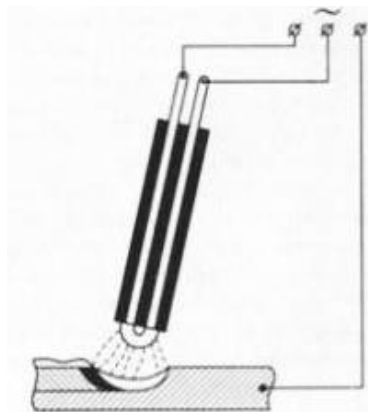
Сварка трехфазной дугой
